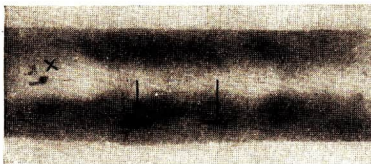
/2. Fehlerhafte Schweißnaht im Röntgenbild
